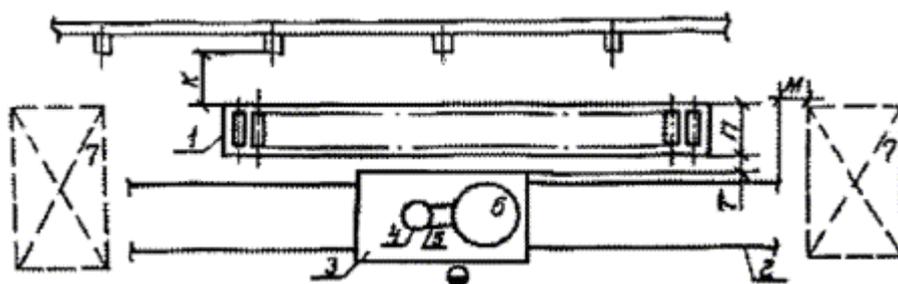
Размещение установки электрошлаковой сварки:
